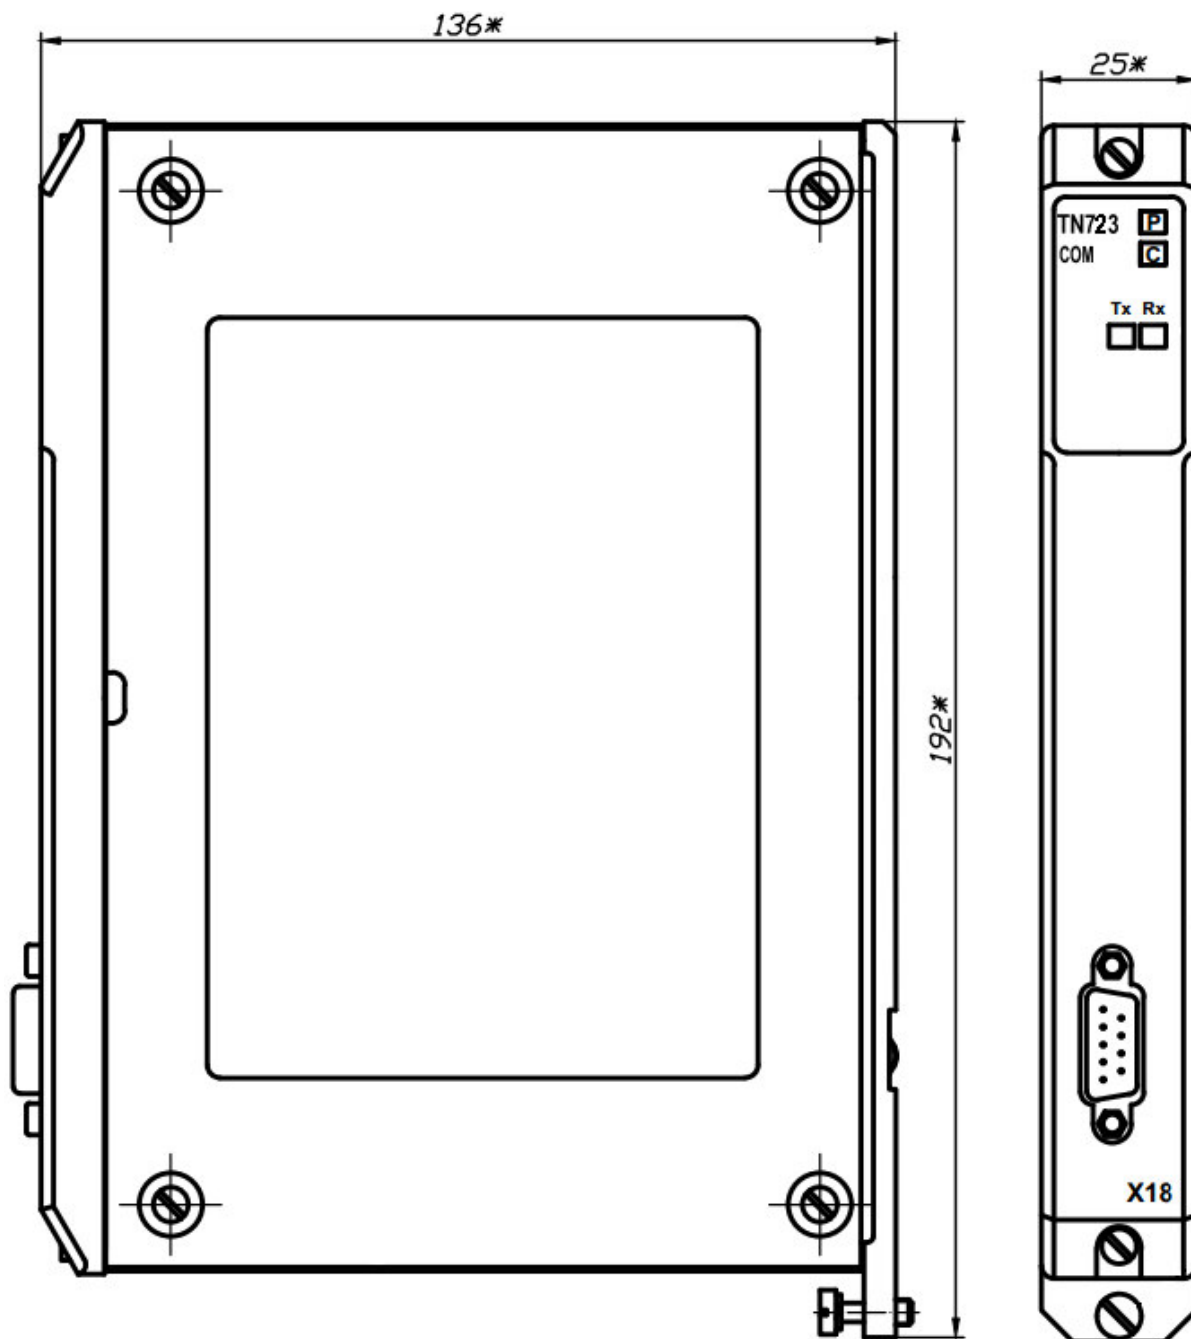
Модуль TN 723. Внешний вид и габаритные размеры
